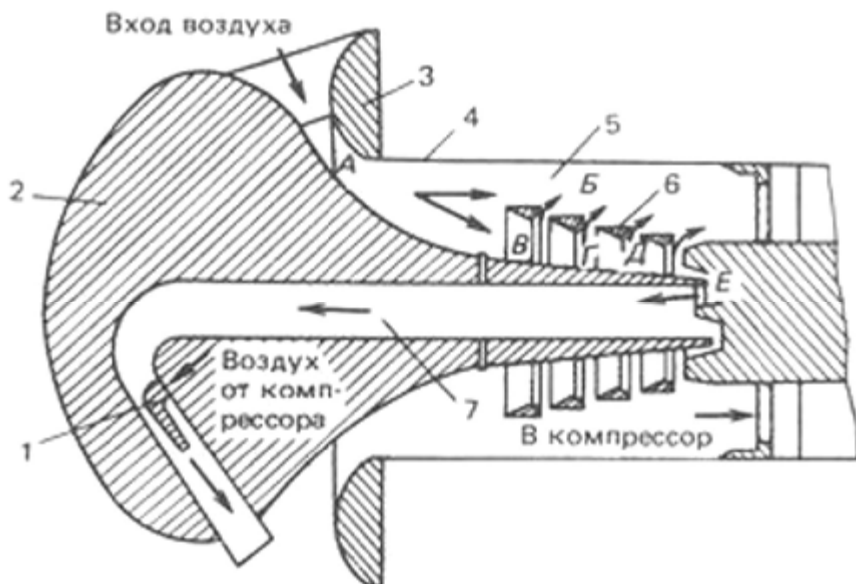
Схема работы пылезащитного устройства двигателей.
